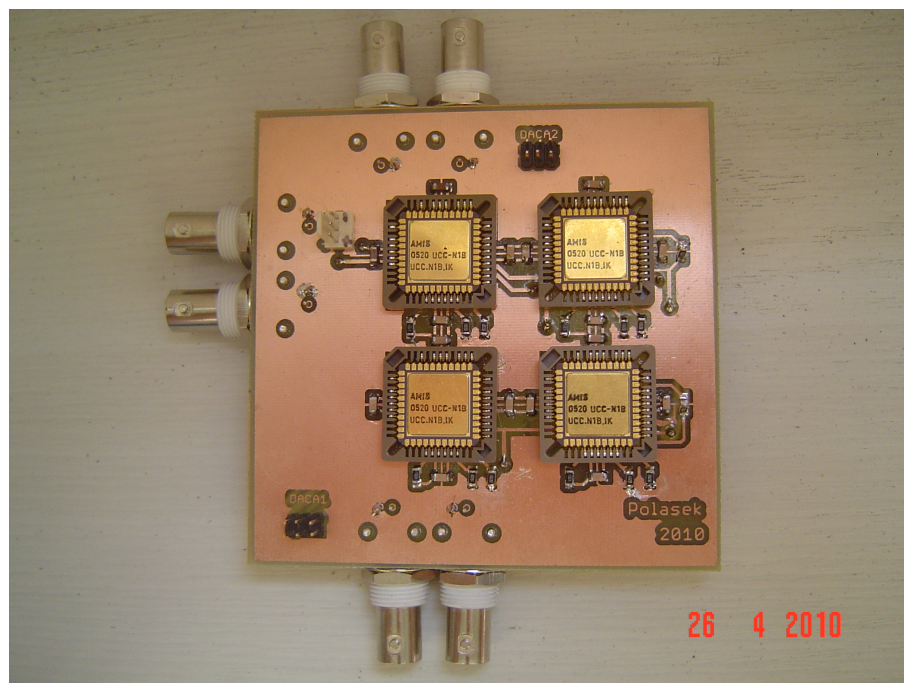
Zadní strana desky plošných spojů (BOTTOM)
